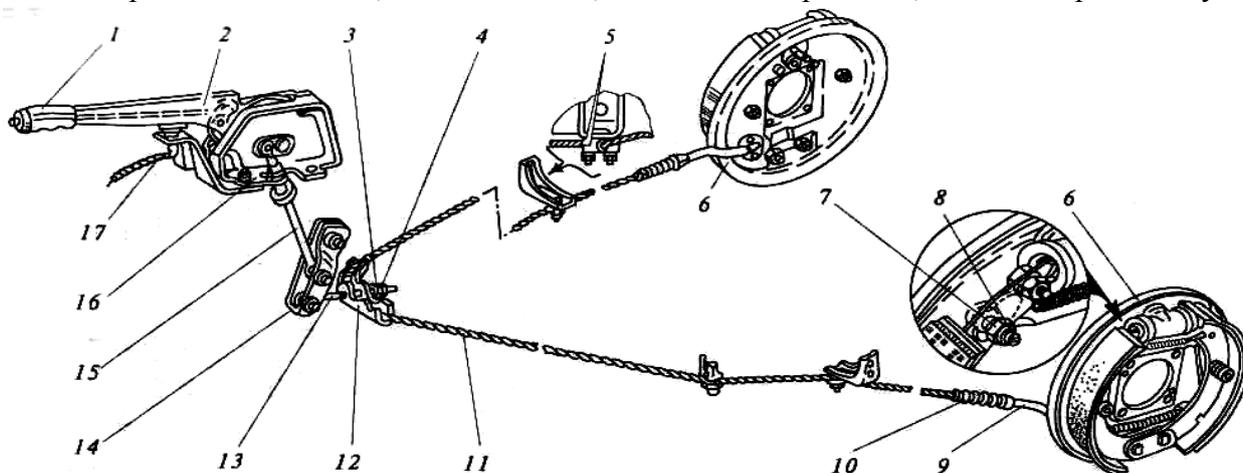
Стояночный тормоз: 1 — ручка; 2, 14 — рычаги; 3, 7 — гайки; 4 — контргайка; 5 — направляющие троса; 6 — задний тормозной механизм; 8 —
